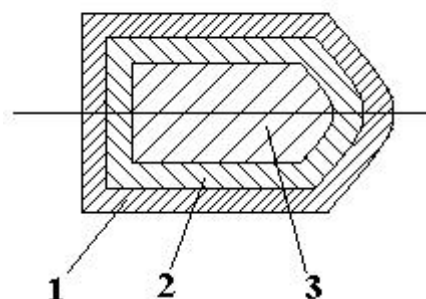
Схема твердосплавного зубка після обробки: 1 – приповерхневий шар; 2 – перехідний шар; 3 – серцевина
